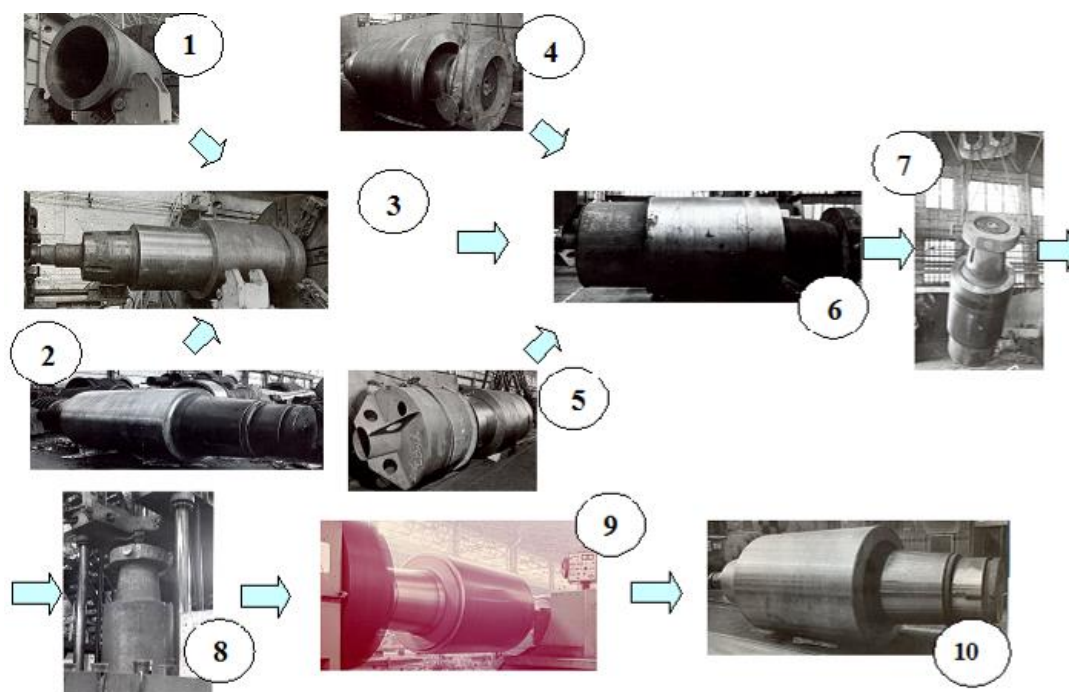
Схема основних операцій реінжинірингу моноблочного вальцювального валка в складеному виконанні
